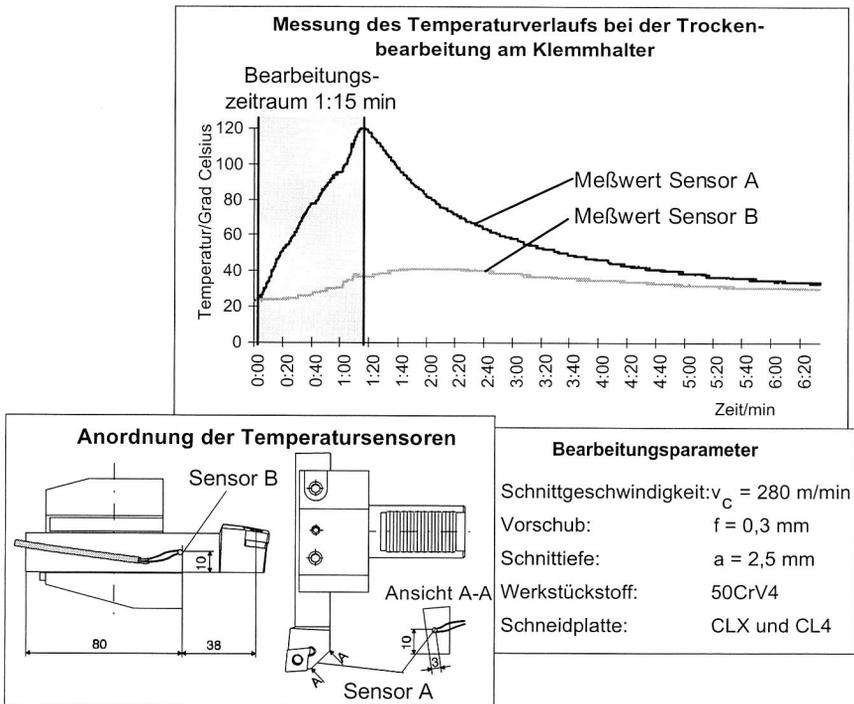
Temperatureintrag in den Klemmhalter eines Drehwerkzeugs bei der Trockenbearbeitung
